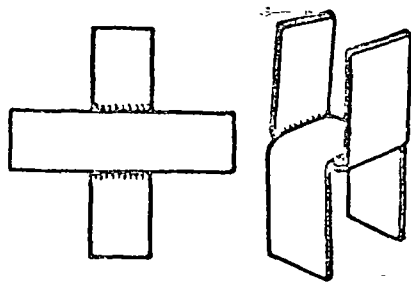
Ensayo de soldabilidad por unión en cruz.
